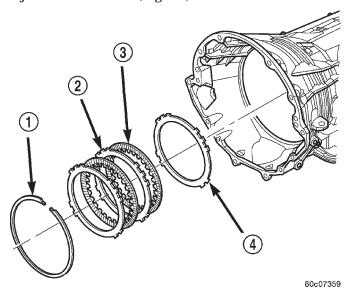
Desmontaje del conjunto de embrague de 2ª
